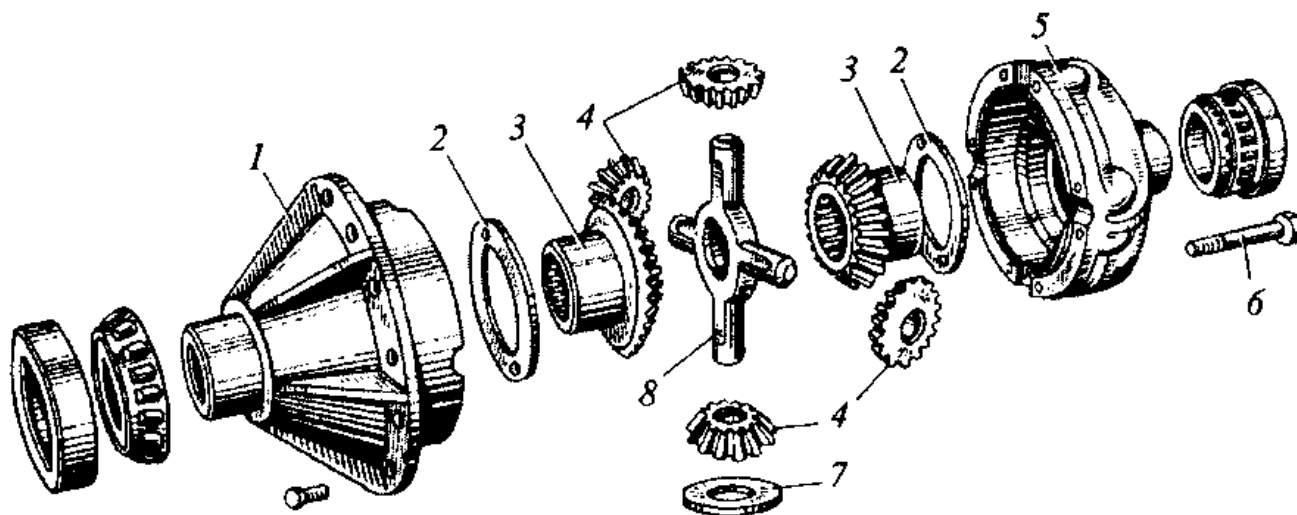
Деталі симетричного диференціала: 1, 5 - чашки диференціалу; 2, 7 - шайби; 3 - півосьові шестерні; 4 - сателіти; 6 - болт кріплення чашок диференціалу; 8 - хрестовина.
